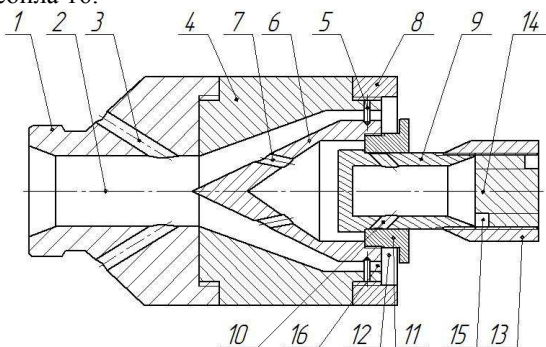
Новий пристрій для гідродинамічного промивання дренажних трубопроводів: 1 – штуцер; 2 – канал підведення води; 3 – реактивні сопла; 4 – корпус; 5 – фіксатори; 6 – обтікач; 7 – забірні канали; 8 – кільцева насадка; 9 – додатковий рухомий корпус; 10 – бічні отвори; 11 – втулка; 12 – проточка; 13 – муфта; 14 – вихрове сопло; 15 – гвинтові канали; 16 – кільцеве щілинне сопло
